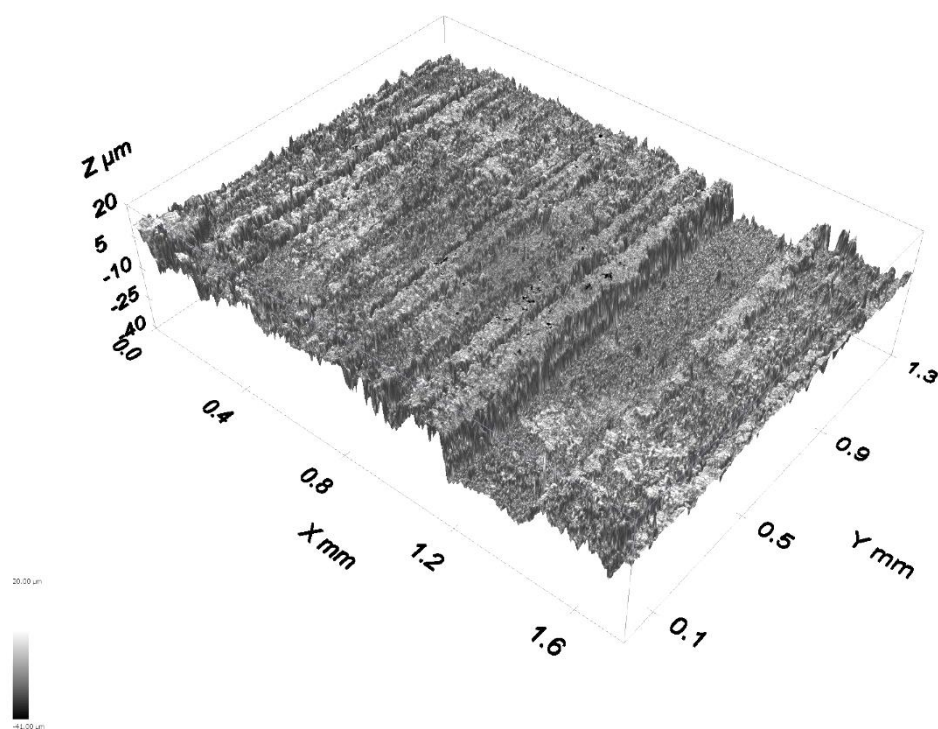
Imagem tridimensional da superfície da cabeça do parafuso.
